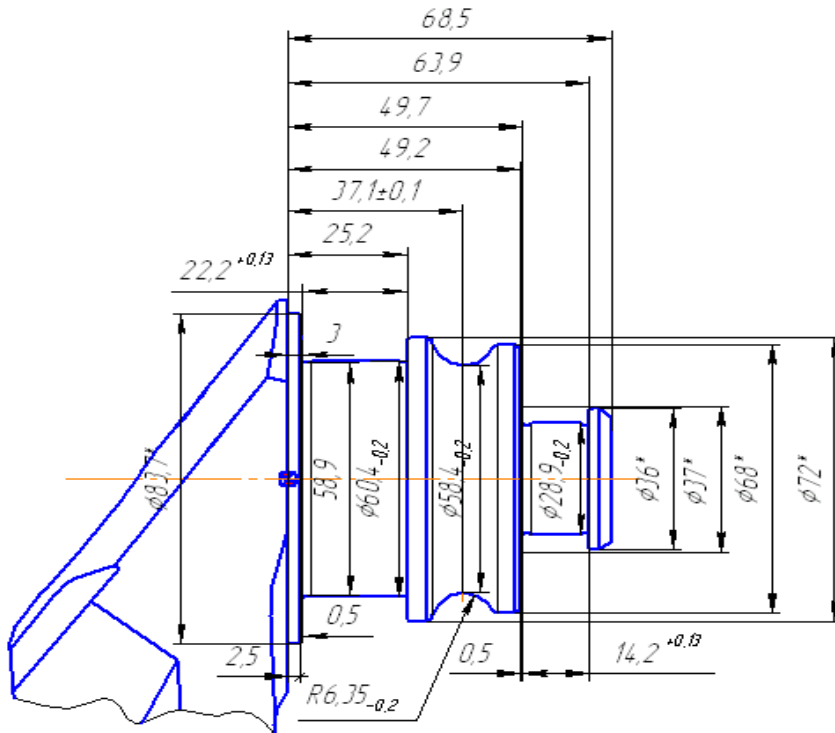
Цапфа-опора лапы, размеры готовой детали
